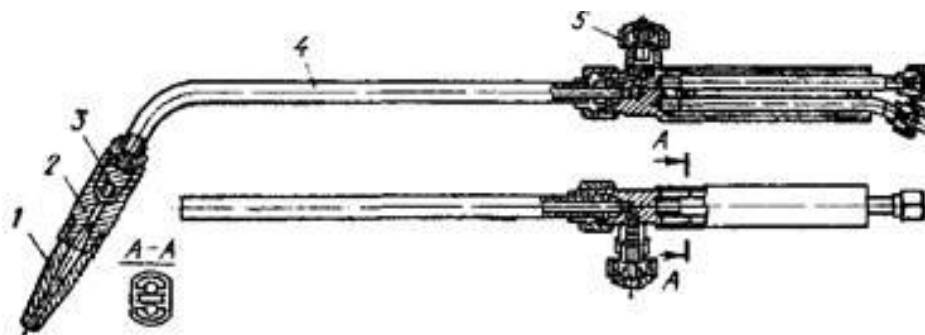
Конструкция сварочной горелки ГС-4:
